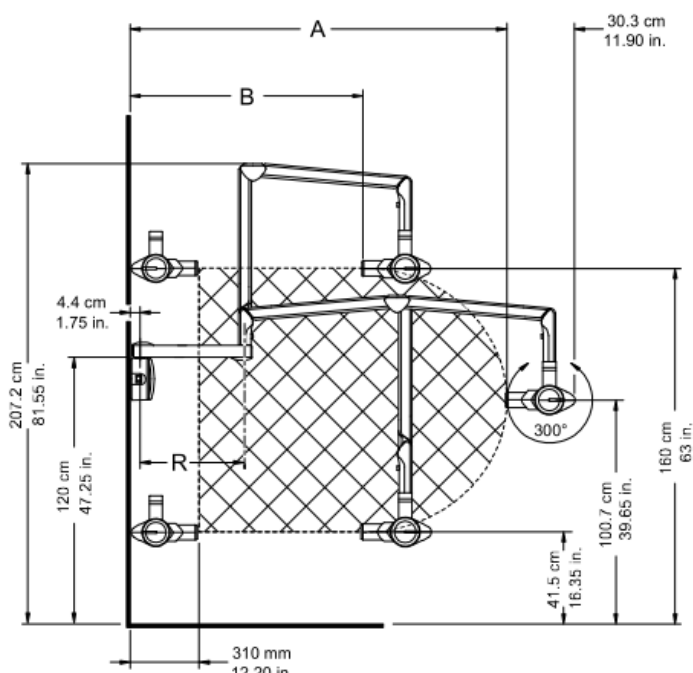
Aparat opcja z pionowo instalowaną płytą montażową
